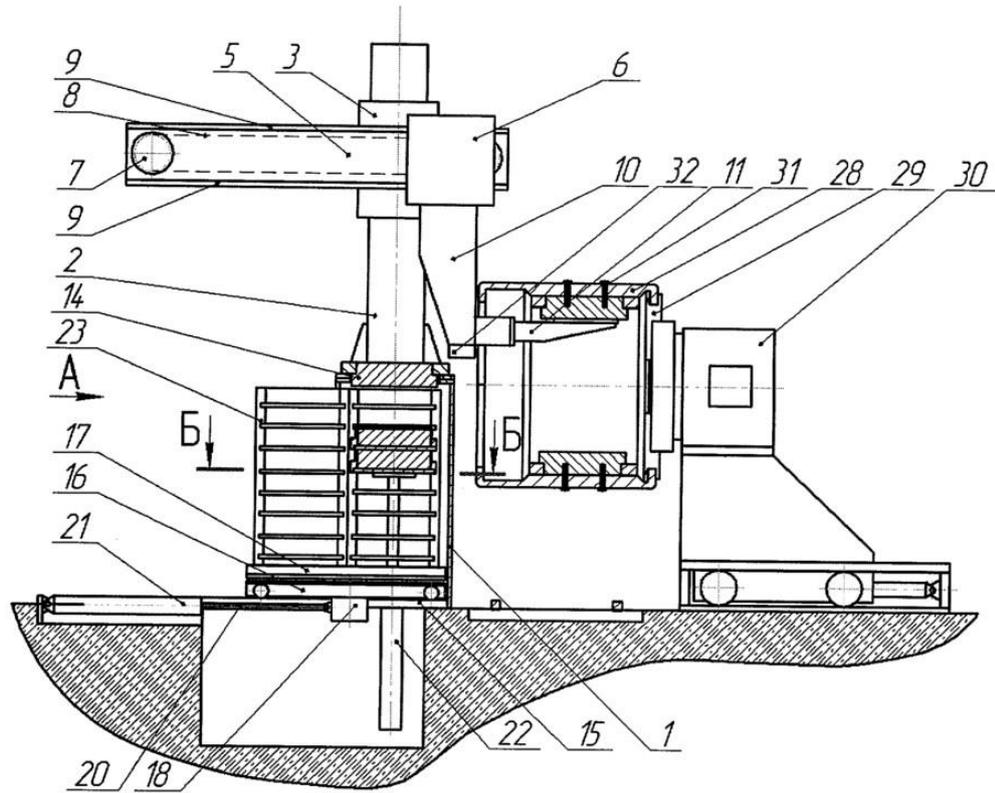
Общий вид станда разборки магнитной системы
